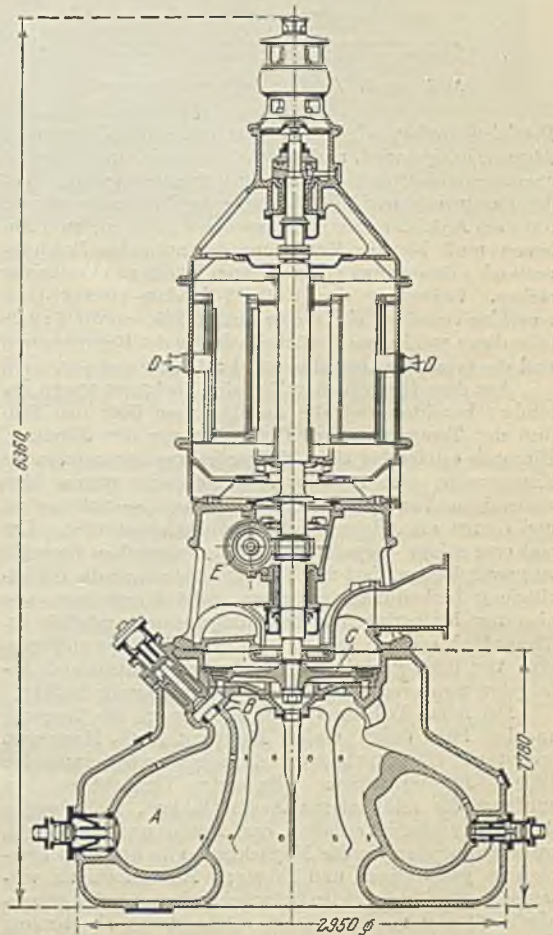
Schnitt durch die Gasturbine. Holzwarth-Junghans.
